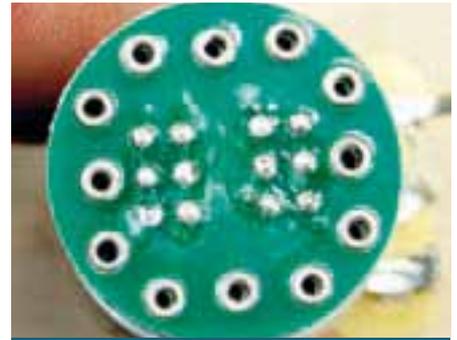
Die Bodenplatte des S1-Schalters mit der Platine
